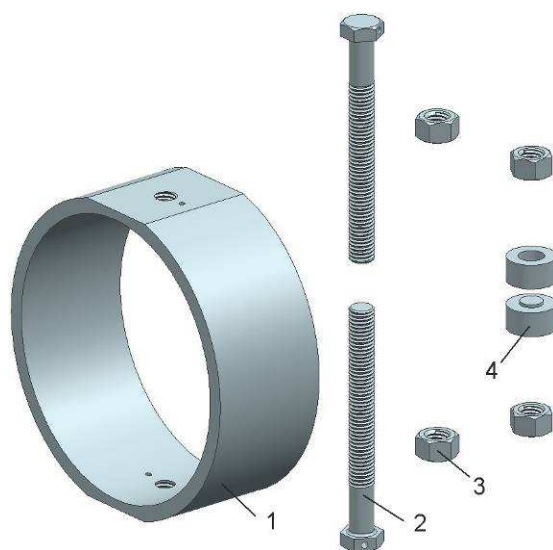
Трехмерные модели элементов приспособления для получения прижимных усилий: 1 – кольцо; 2 – болт; 3 – гайка; 4 – прижимные головки
